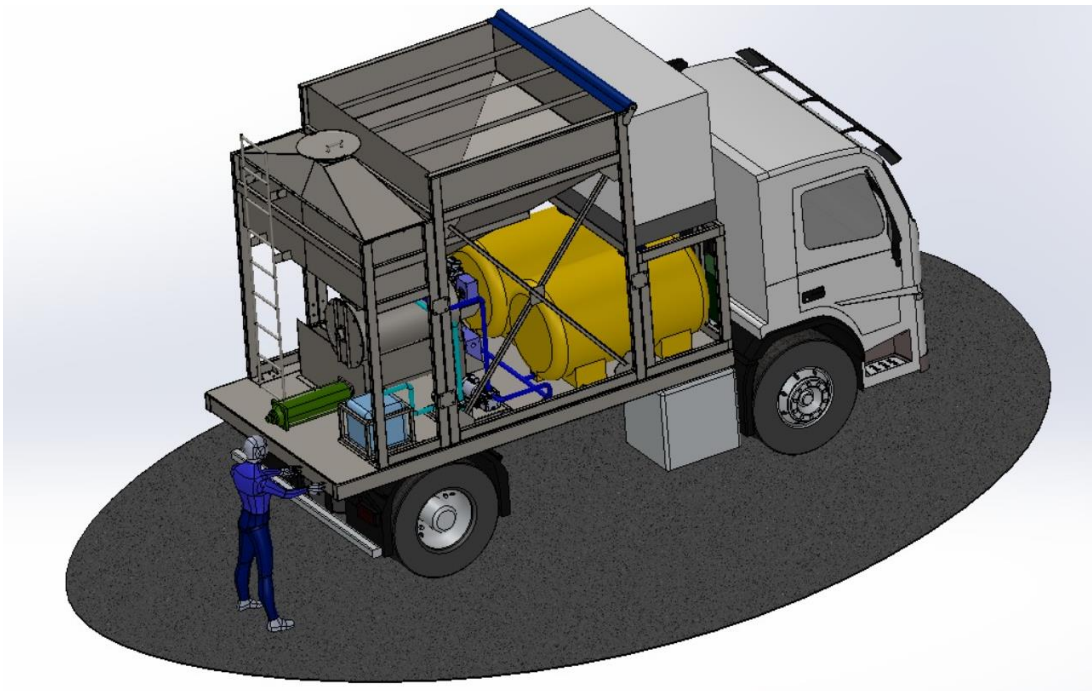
vista del diseño final de la planta móvil. SolidWorks.
